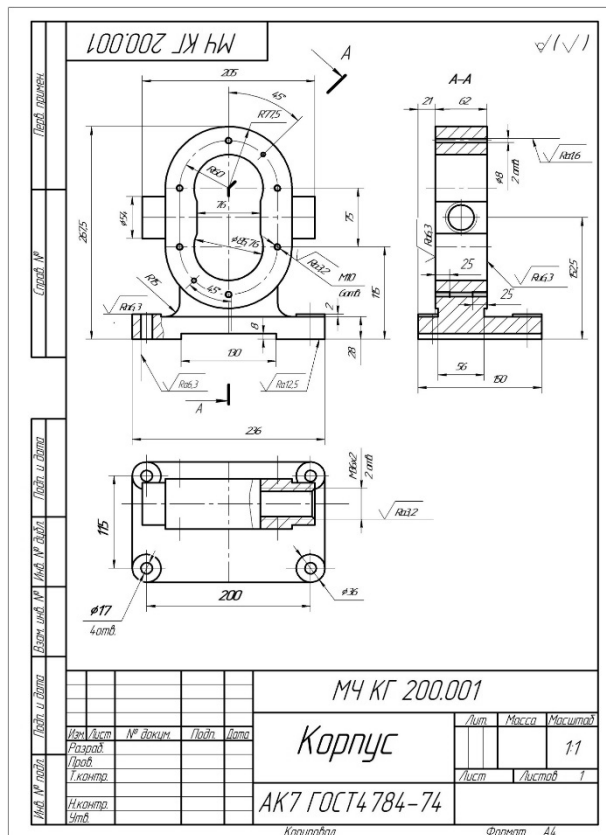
Рабочий чертёж «Корпус», позиция 1
